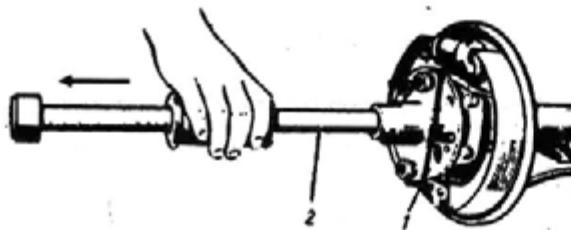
Выпрессовка полуоси с помощью ударного съемника:
